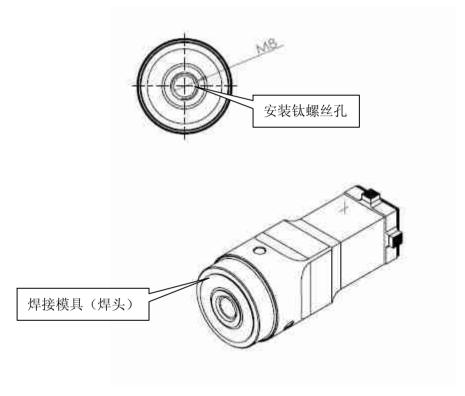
焊接模具 (焊头) 示意图
